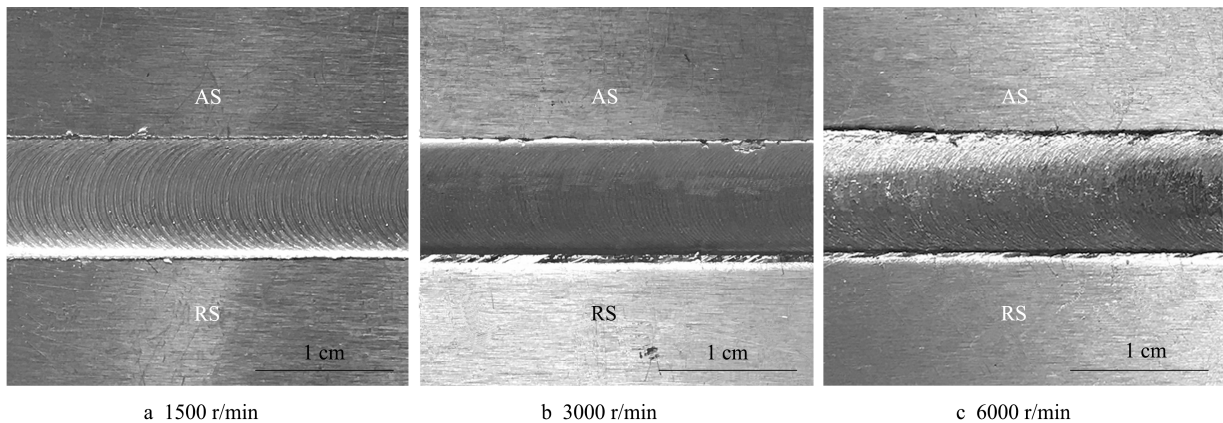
焊速900 mm/min时搭接接头焊缝表面宏观形貌
